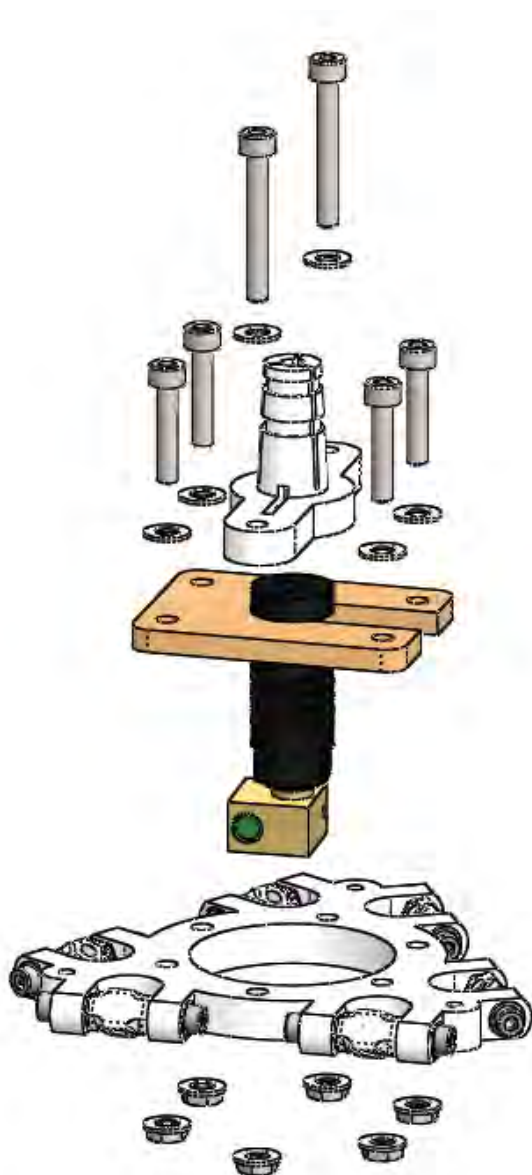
Componentes ensamble J-Head con *Plataforma*.
